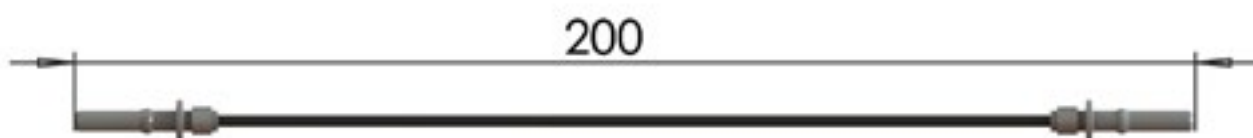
Внешний вид и габаритные размеры оптической перемычки
